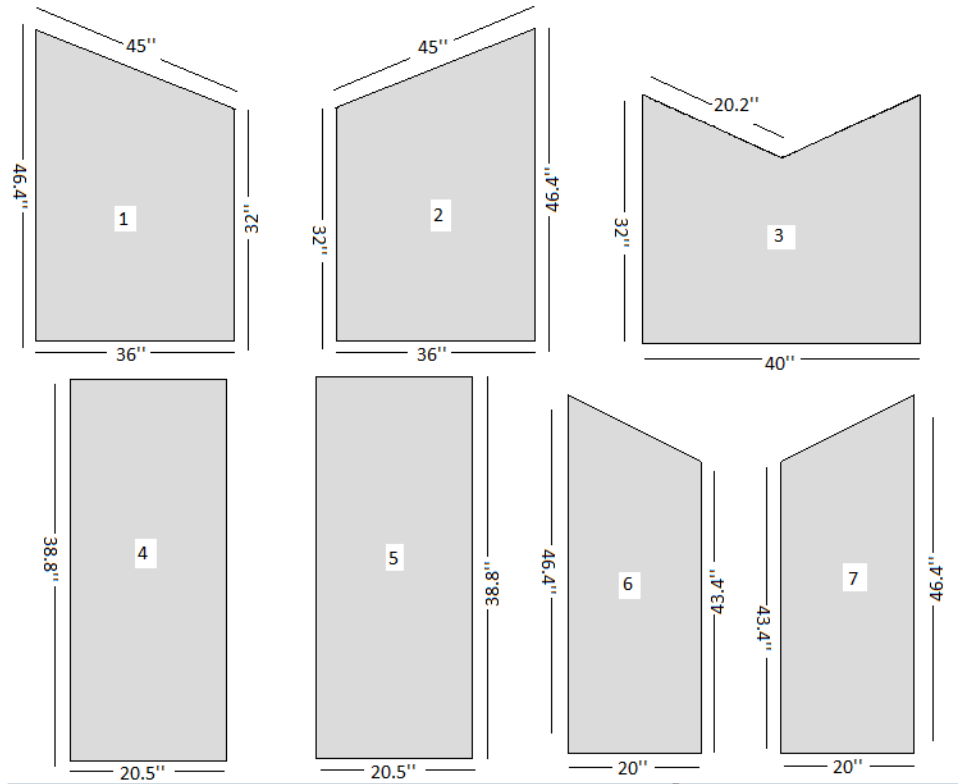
Étape 1 : Dimensions des morceaux à découper du prototype 3
